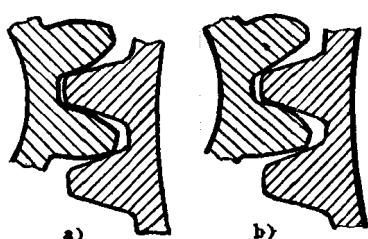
11 螺旋锥齿轮与双曲面齿轮法向齿面形状的比较
